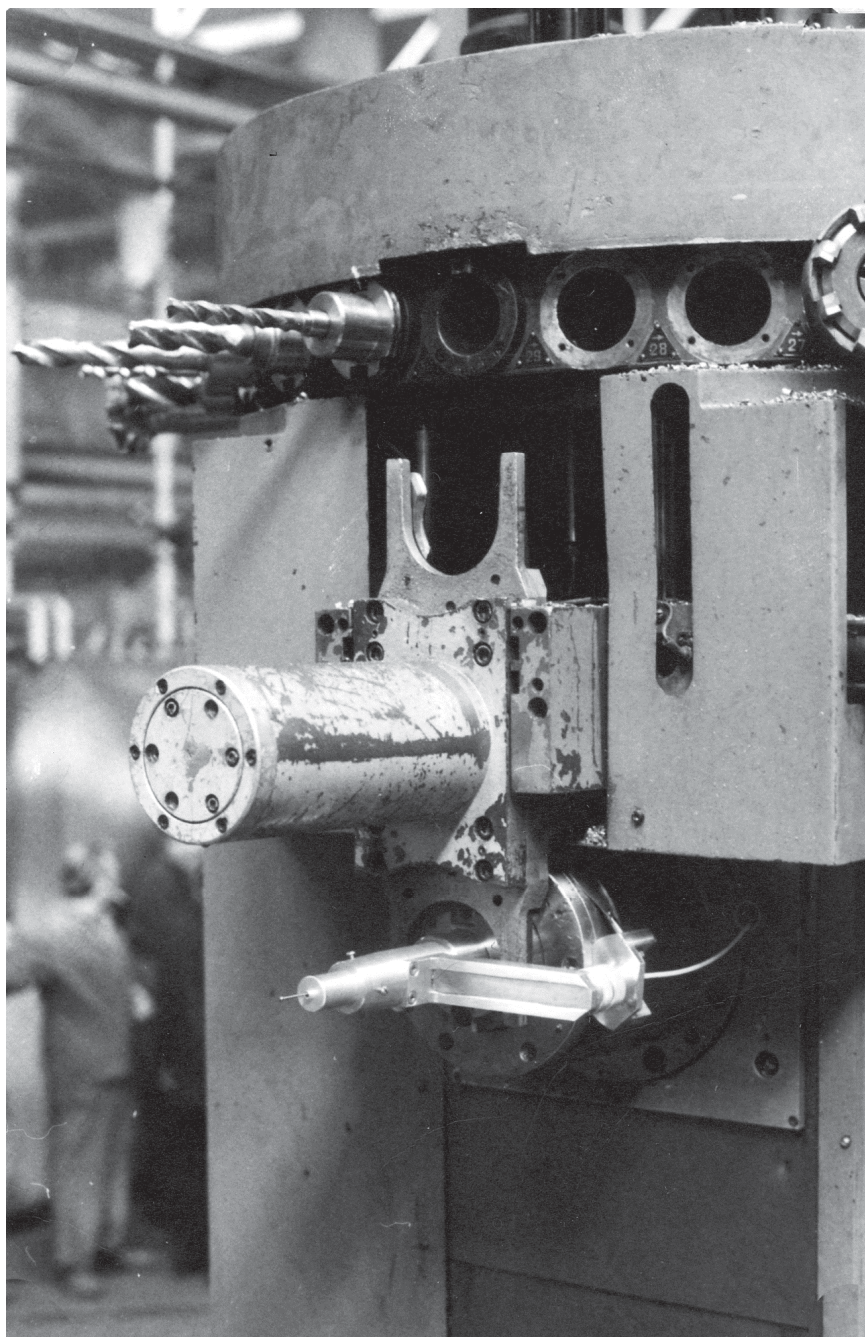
Измерительный модуль установлен в шпиндель станка
